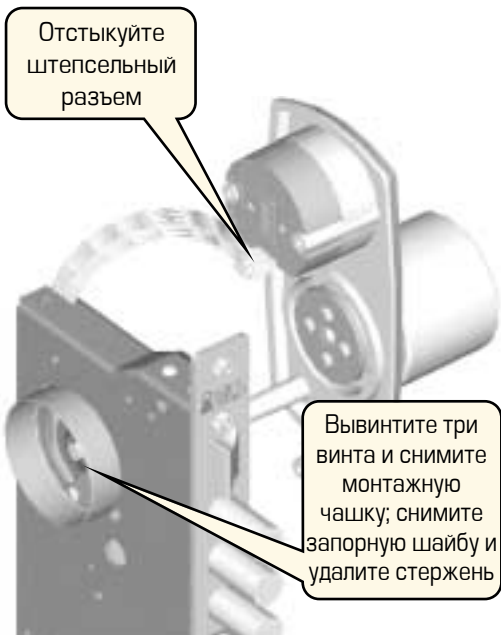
Снятие наружной ручки с накладкой и монтажной чашки
